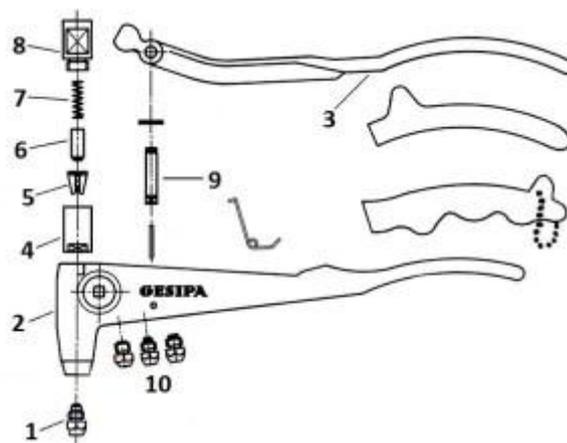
Конструкция заклепочных клещей: 1 – головка; 2 – корпус; 3 – верхняя рукоятка; 4 – рабочая втулка; 5 – цанговые кулачки; 6 – конусная втулка; 7 – пружина; 8 – крышка; 9 – ось; 10 – комплект сменных головок
